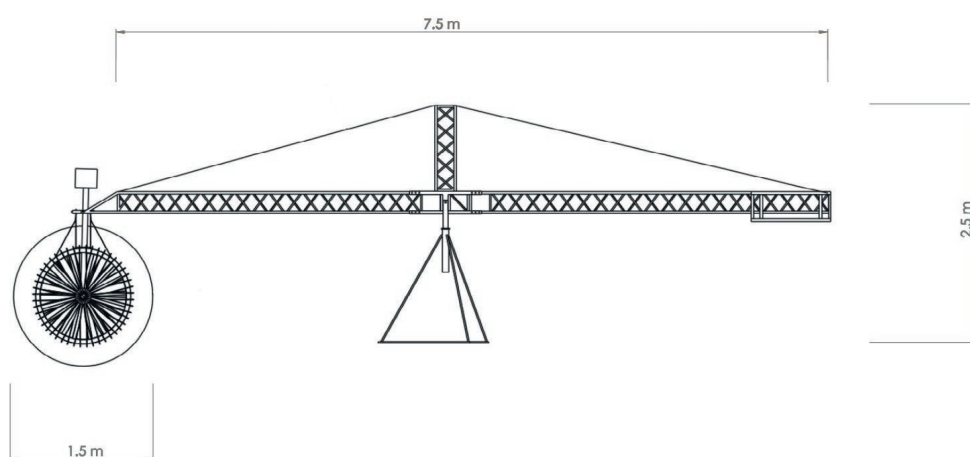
esquemático da turbina geração 2 em vista frontal com esboço geral de dimensões.
